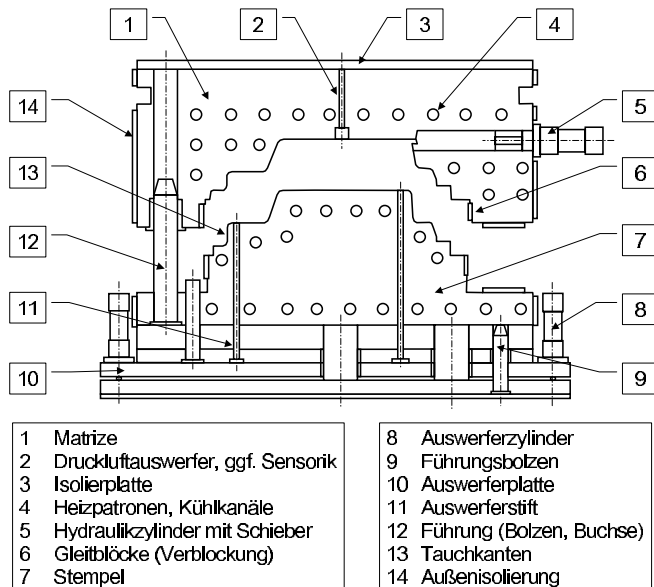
Typisches GMT-Presswerkzeug [4]
